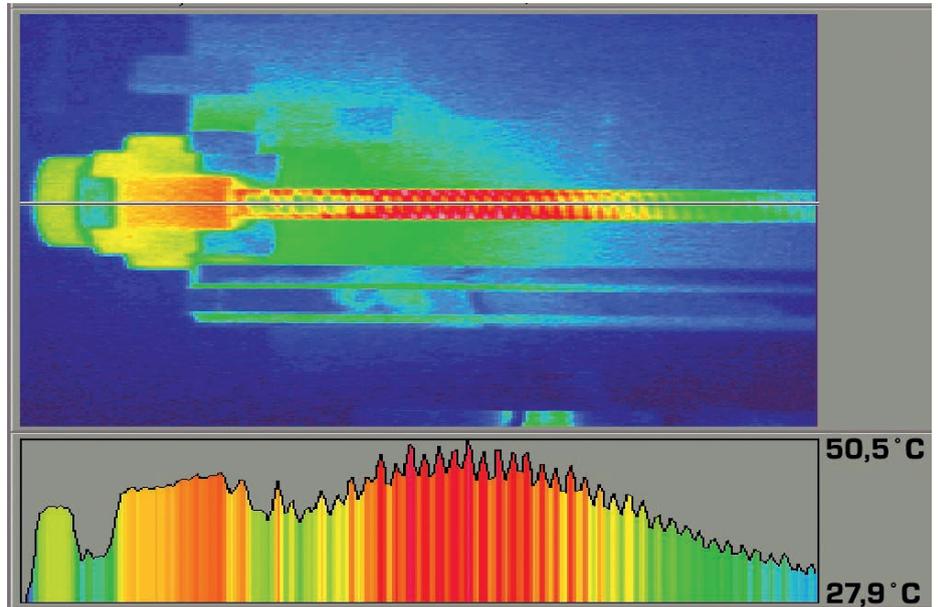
Lokale Erwärmung einer Kugelgewindespindel im Verfahrensbereich der Kugelgewindemutter nach 6-stündigem Reversierbetrieb mit 24 m/min zwischen zwei 150 mm voneinander entfernten Punkten (vgl. A. Frank / F. Ruech: Position measurement in CNC Machines). Für diese Thermografieaufnahme wurde der Maschinentisch am Ende des Verfahrenprogramms zur Seite gefahren. Zu erkennen ist der Riemenantrieb, das Festlager und die Kugelgewindespindel.
